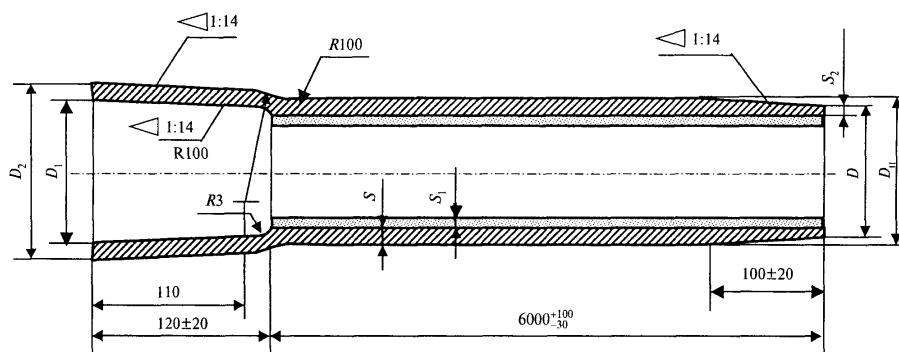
Схема трубы под нахлестное сварное соединение
